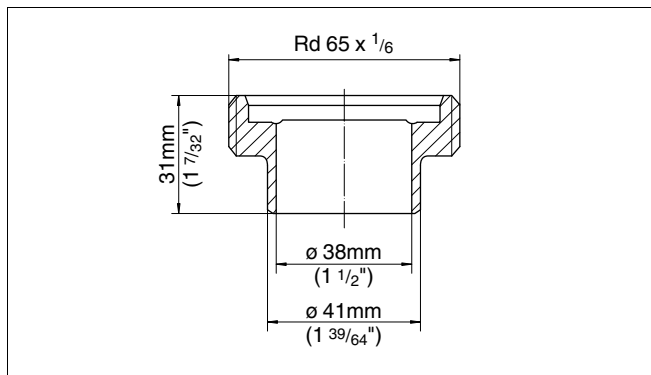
Medidas racor soldado DN 40 según DIN 11864-1
